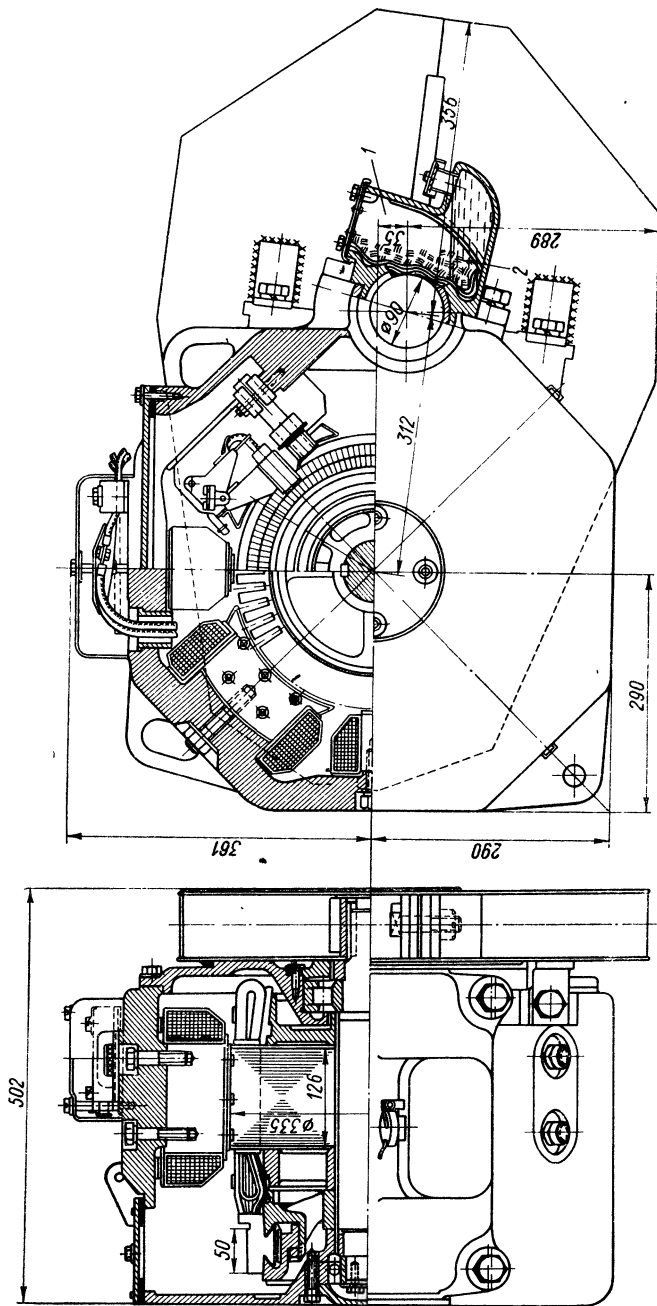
Цельнокорпусный тяговый двигатель рудничного электровоза
